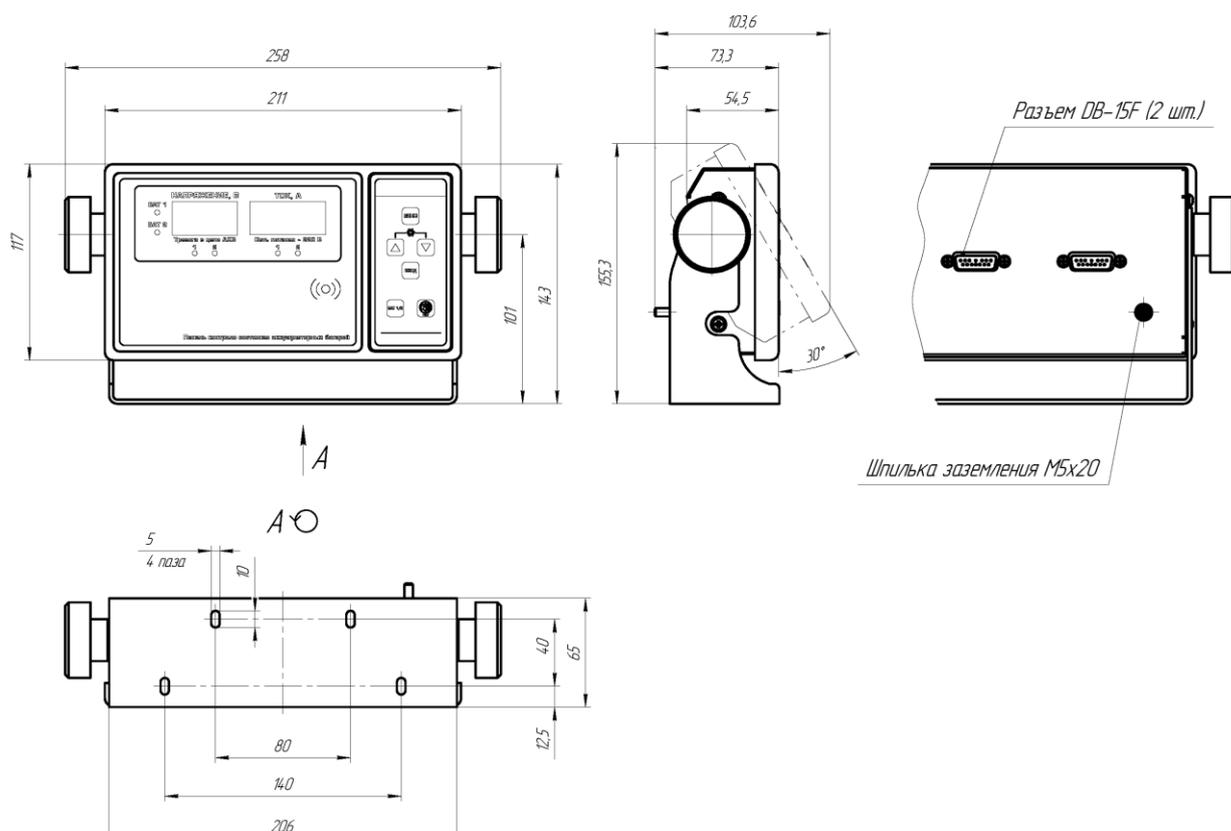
Габаритные и установочные размеры ПКБ-136
